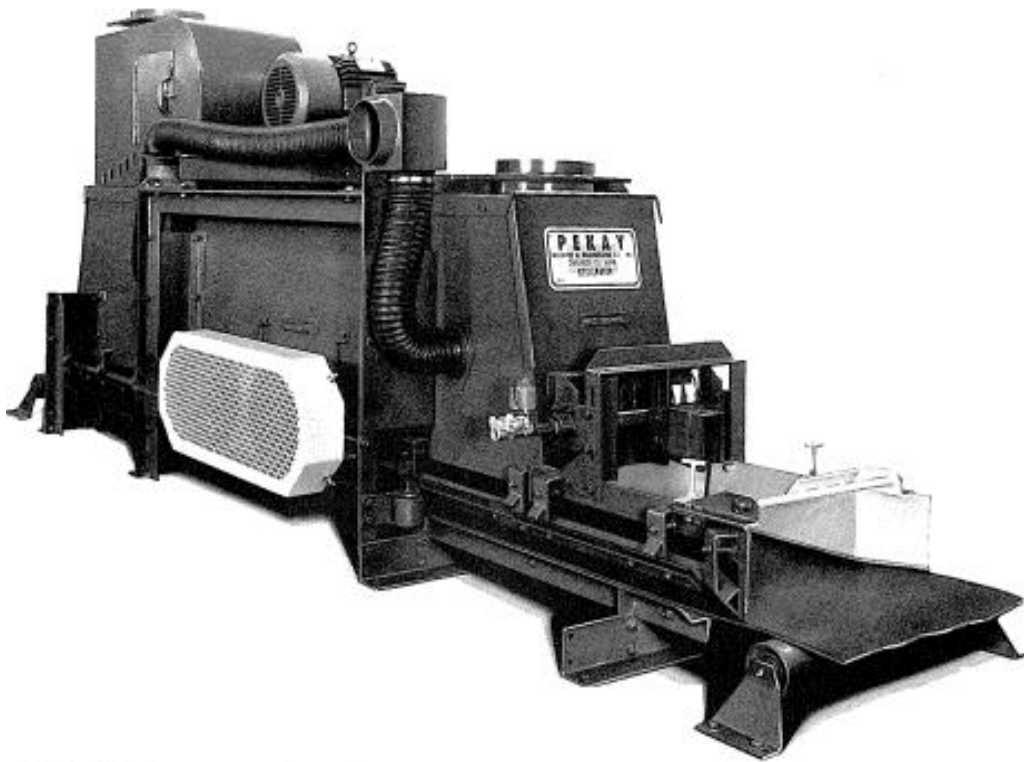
Загальний вигляд роторного змішувача PEKAY Machine & Engineering Co., Inc
